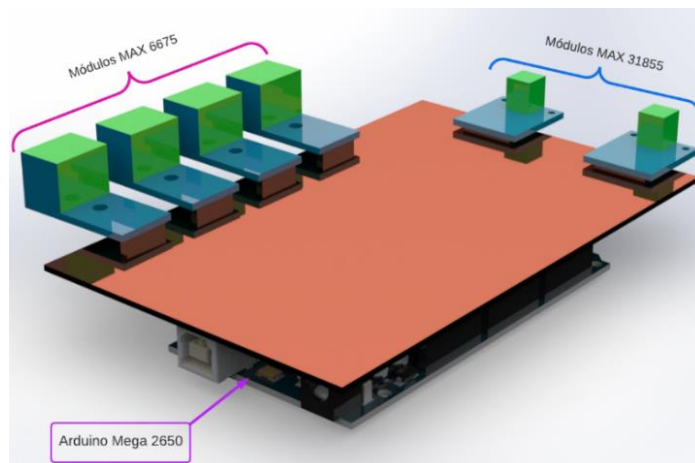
68 Diseño del Prototipo electrónico en 3D
